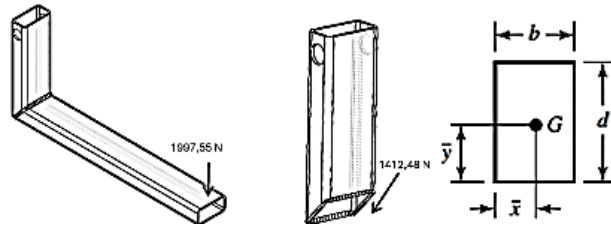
Análisis de la soldadura entre los Elementos 1 y 2.
